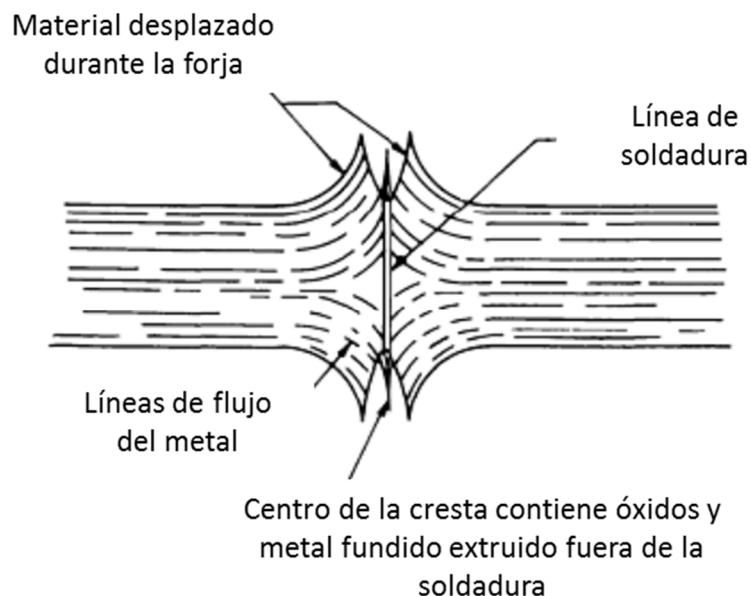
Sección transversal soldadura a tope por destello. (ASM, Flash Welding, 1993)
